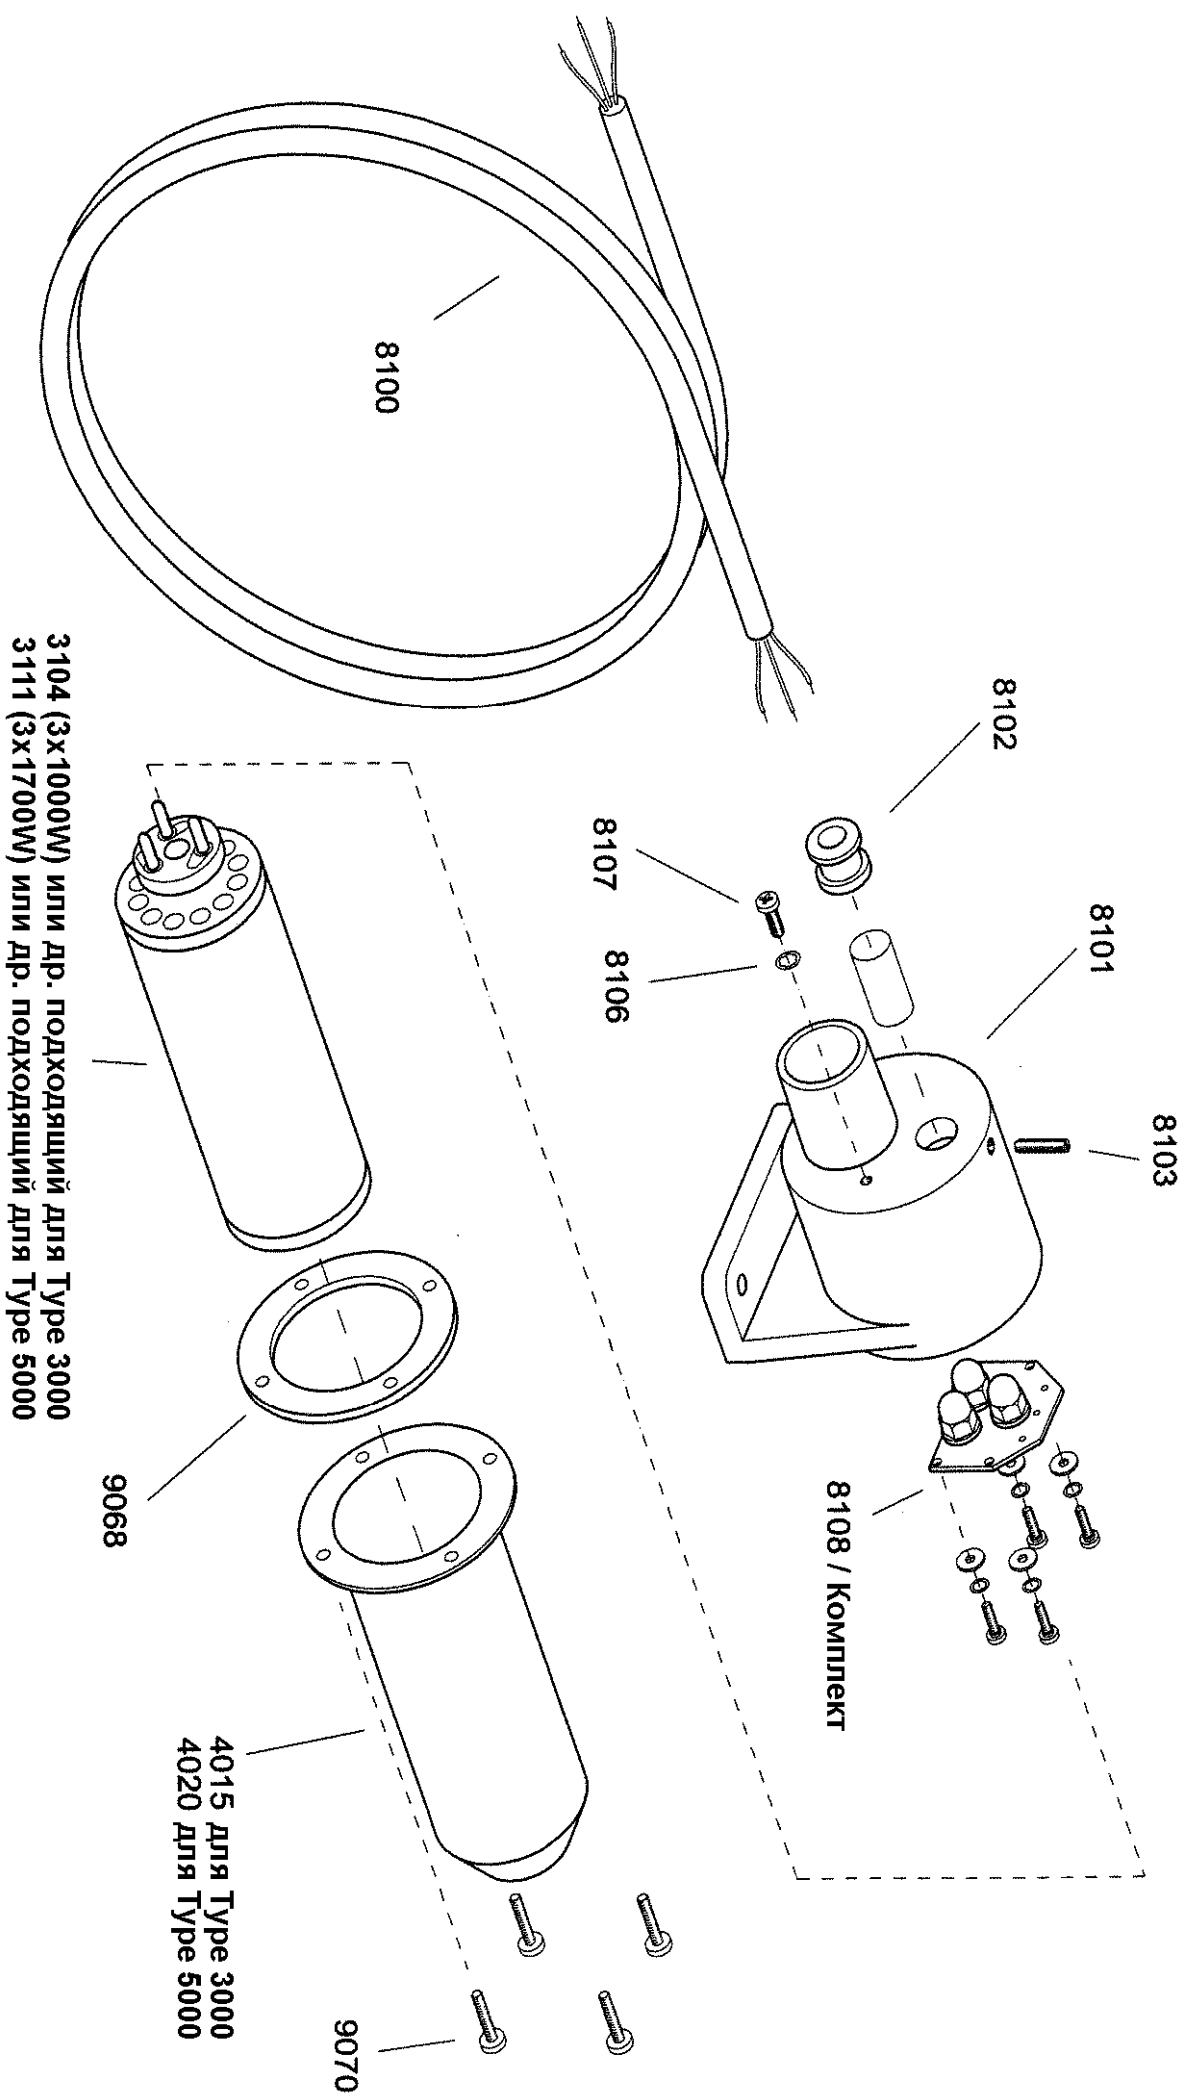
Сборочный чертёж промышленных нагревателей Типе 3000 и Типе 5000
